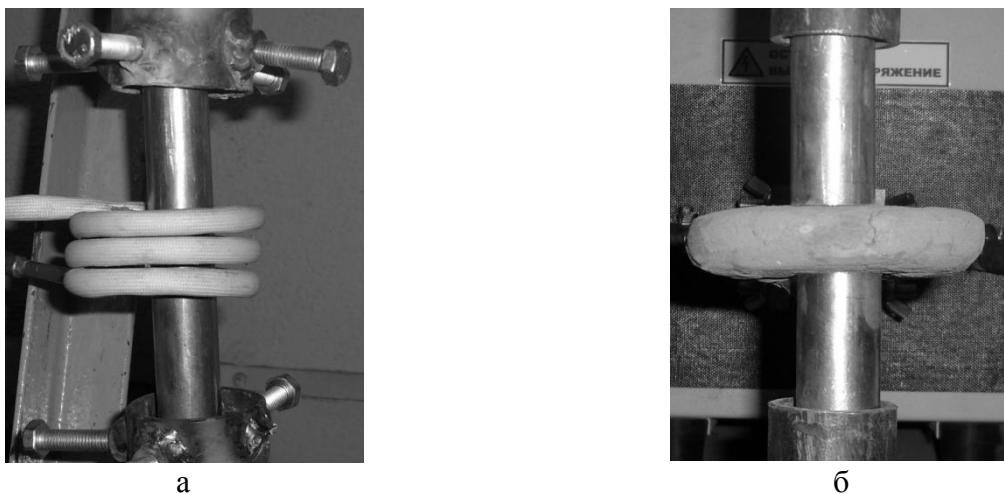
Общий вид индукторов установки индукционно-стыковой сварки: а – наружный индуктор, б – плоский индуктор
